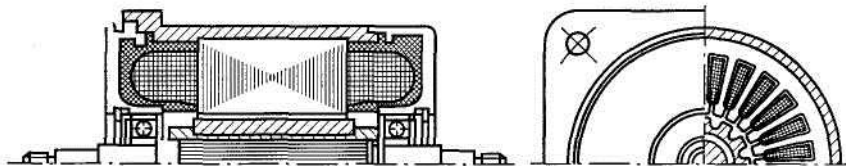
Шаговый двигатель типа ШД-2 с активным ротором в виде магнита-звездочки
